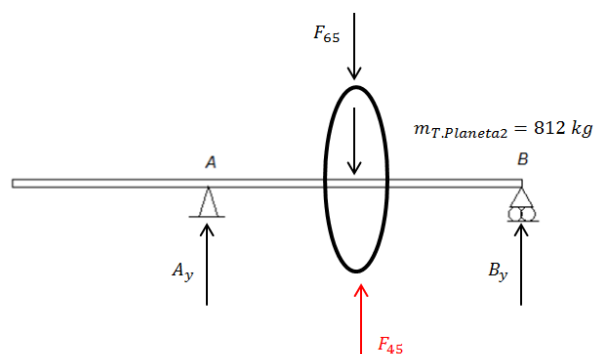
Esquema de fuerzas que actúan sobre el engranaje planeta
